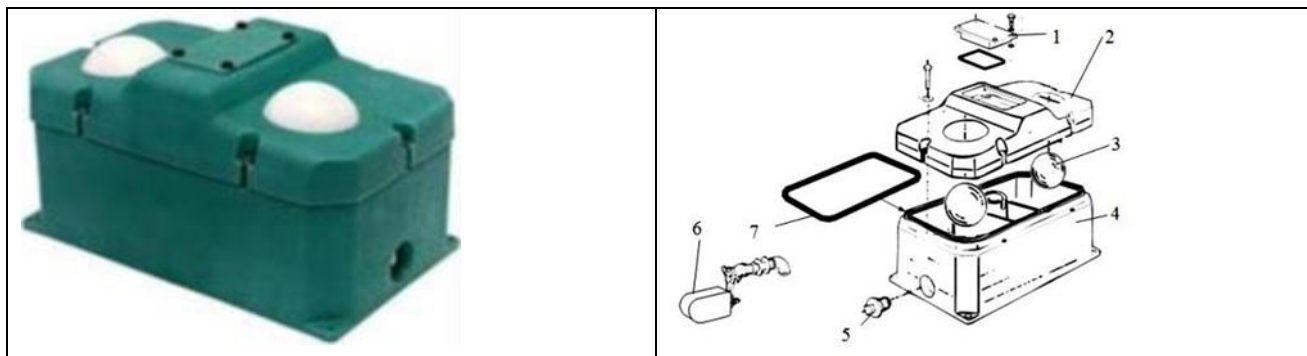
Общий вид и устройство мячевой поилки Suevia 640: 1 - люк; 2 - крышка; 3 - шар; 4 - корпус; 5 - дренажный клапан; 6 - поплавковый механизм; 7 - уплотнительная прокладка
